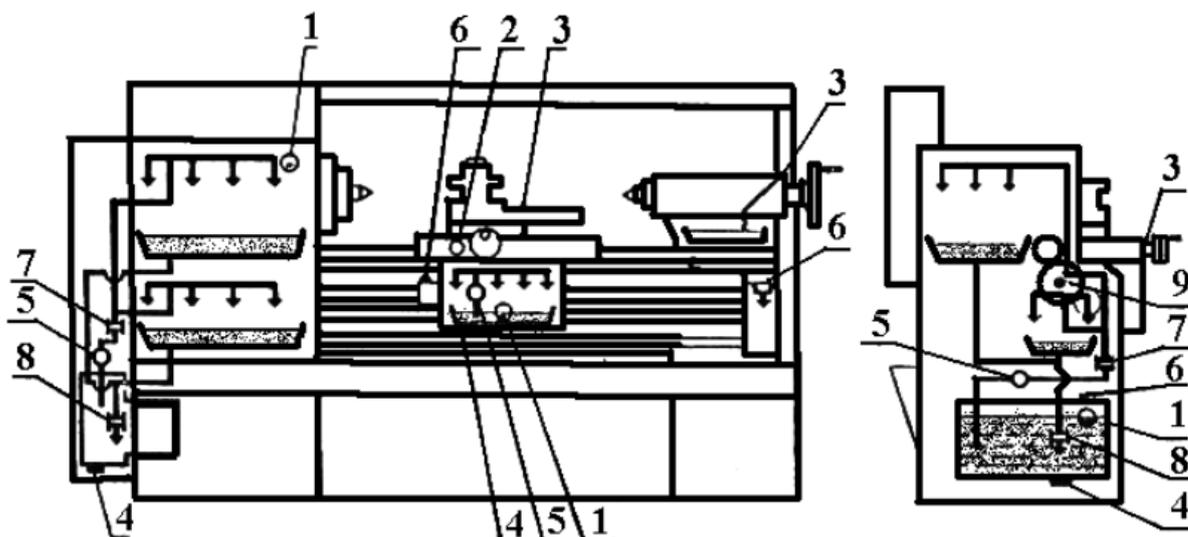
Пример оформления схемы смазки токарного станка
